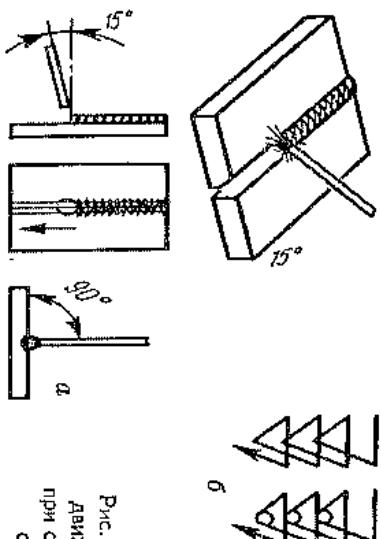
Положение (а) и движение электрода (б) при сварке стыковых швов со скосом кромок
